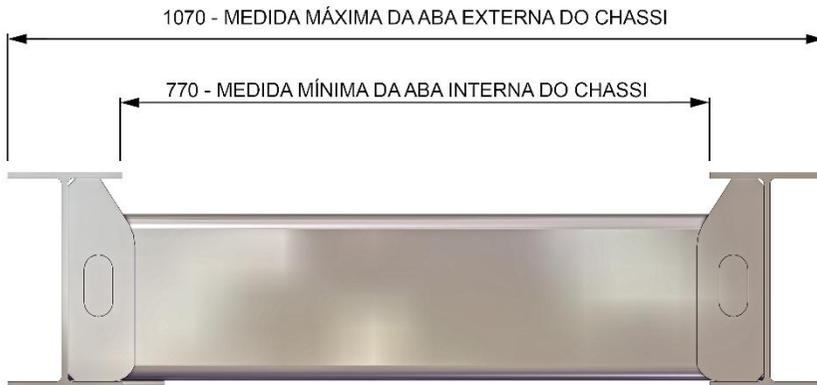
Dimensão do chassi para instalação da AirSteer bitola 1926
